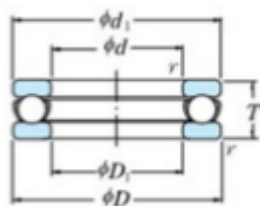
Diseño del rodamiento axial de bolas NSK.
